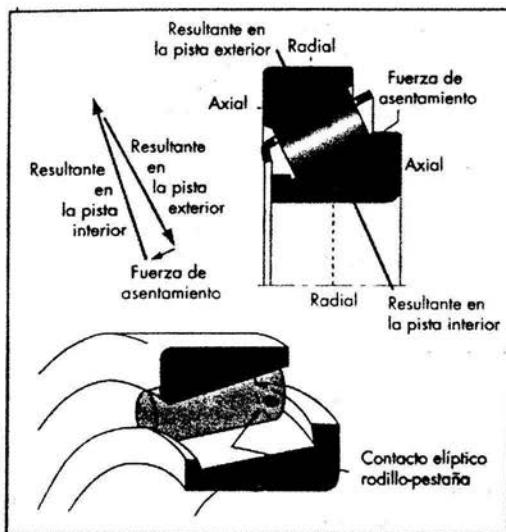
Fuerzas que actúan sobre un rodamiento cónico
